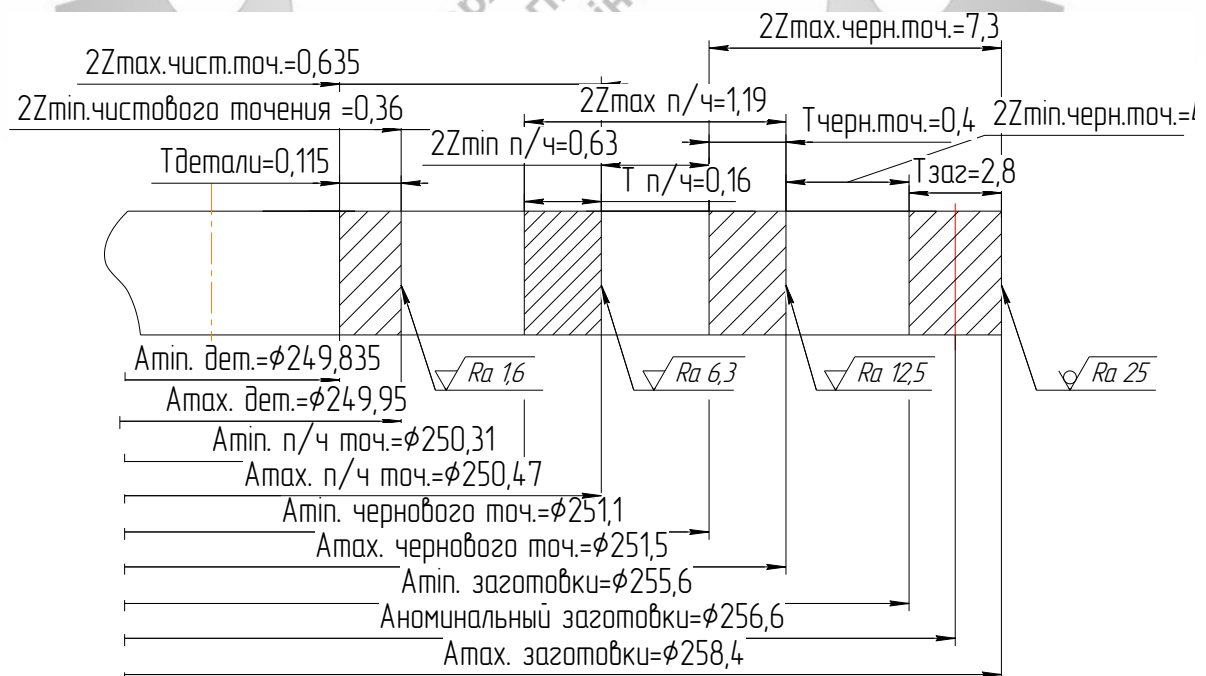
Схема розташування допусків, припусків на оброблення циліндричного розміра $\varnothing 250f9$
